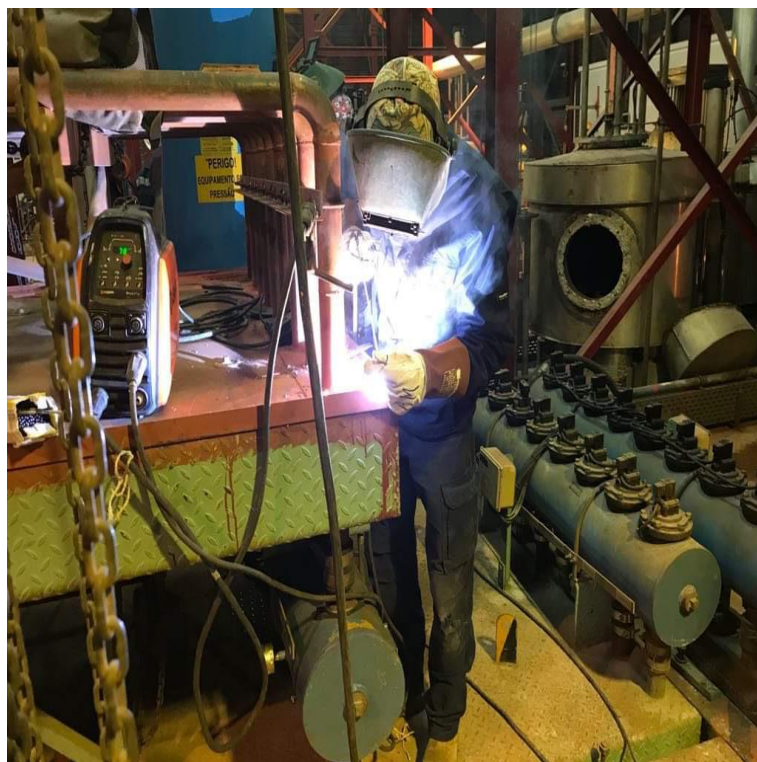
Processo de soldadura com gás inerte de tungsténio
